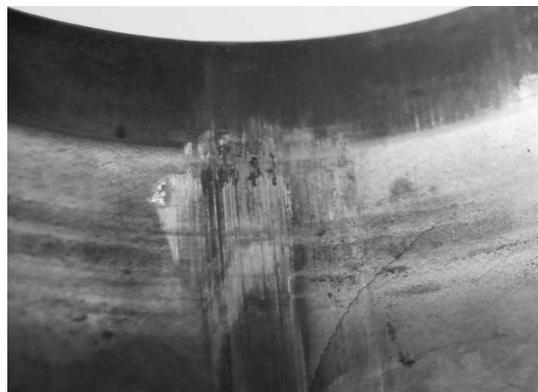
Зеркало разрушенной втулки рабочего цилиндра
